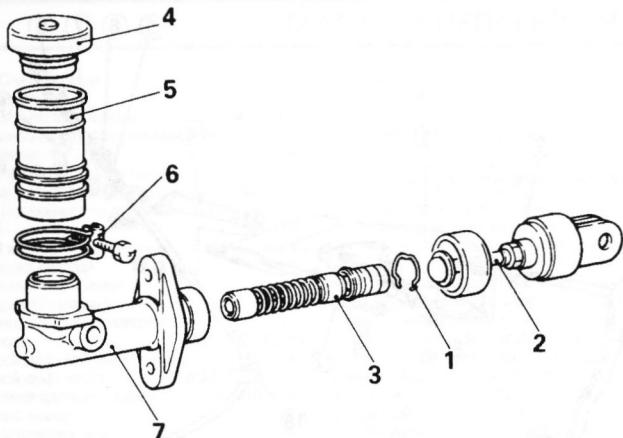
Типичный главный цилиндр сцепления – подробное изображение
